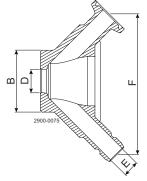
Cuerpo de la válvula: Depósito (para soldar)
